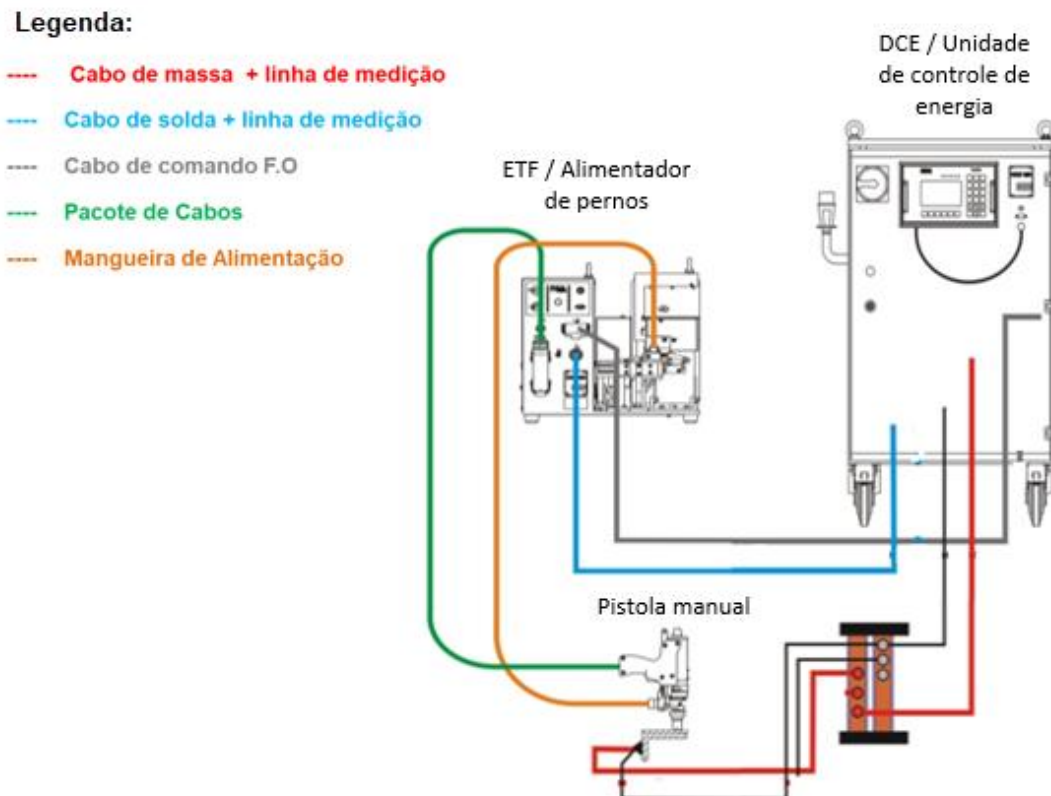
Esquema de instalação do equipamento para soldagem semiautomática.
